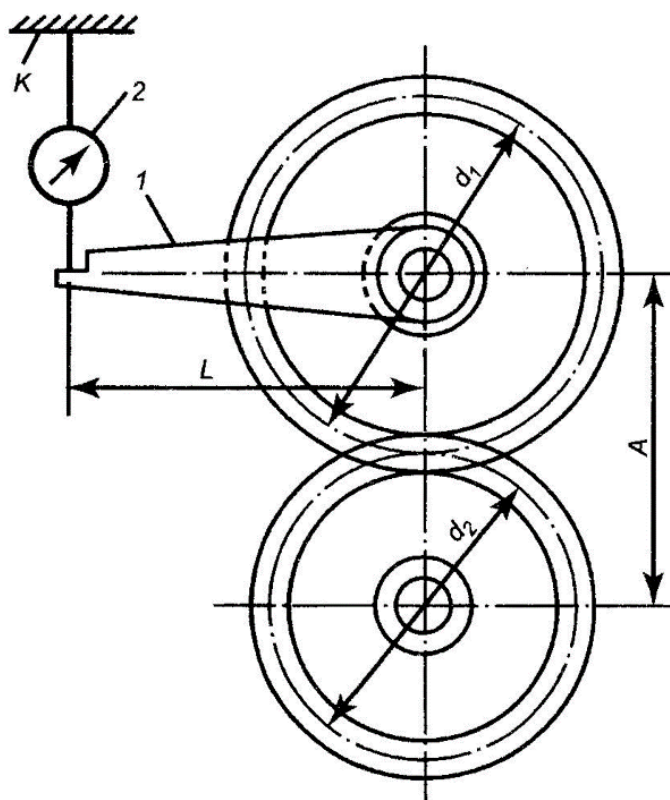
Схема вимірювання бокового зазору індикаторним пристроєм:
